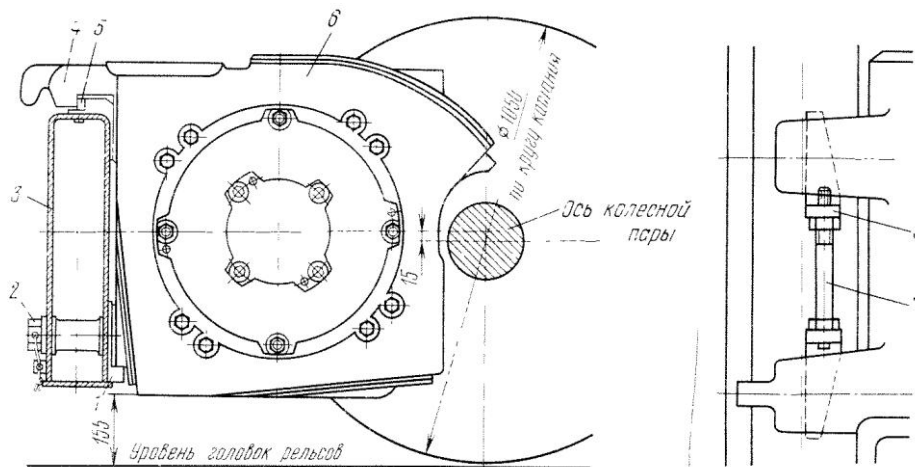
Крепление тягового двигателя на раме тележки моторного вагона
